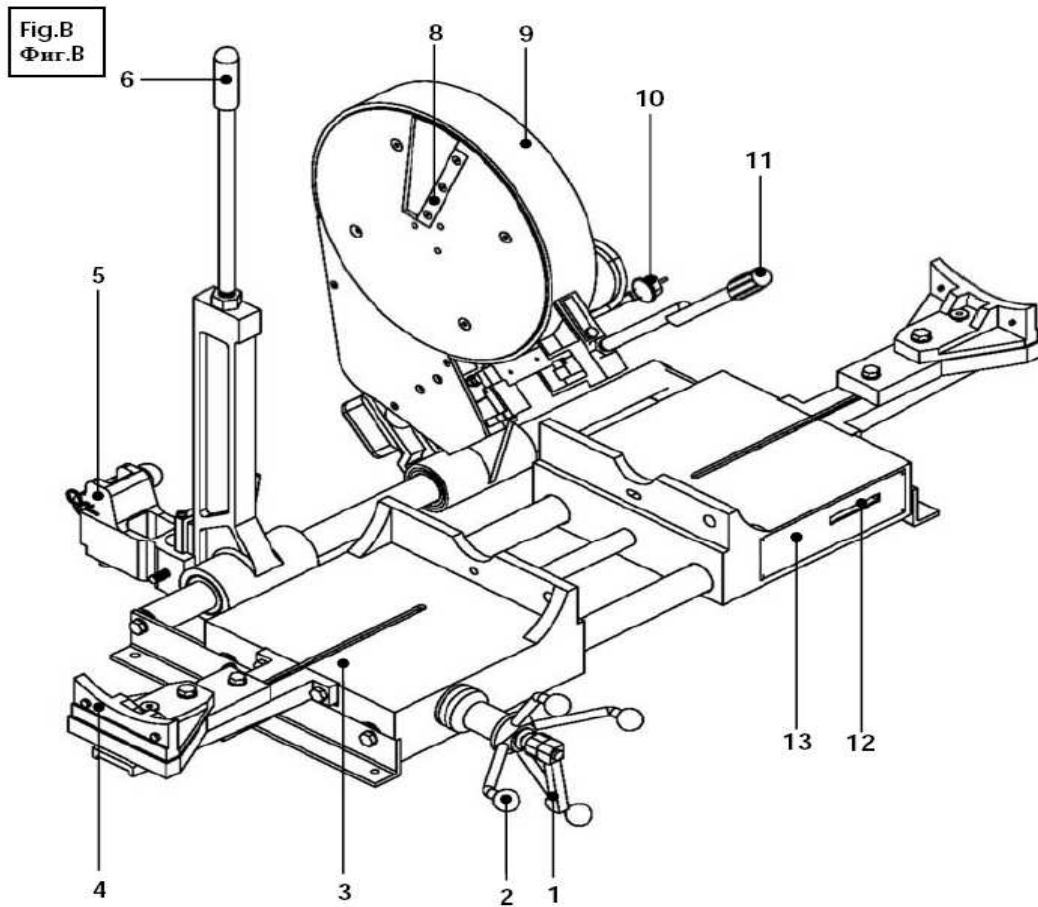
frana, 2- maner actionare carucior, 3- carucior mobil, 4- suport lateral, 5- termoplaca, 6- maneta actionare termoplaca, 7- priza pentru termoplaca, 8- cutit taietor, 9- freza, 10- stecher, 11- maneta, 12- indicator forta de sudura, 13- placa forta de sudura.
